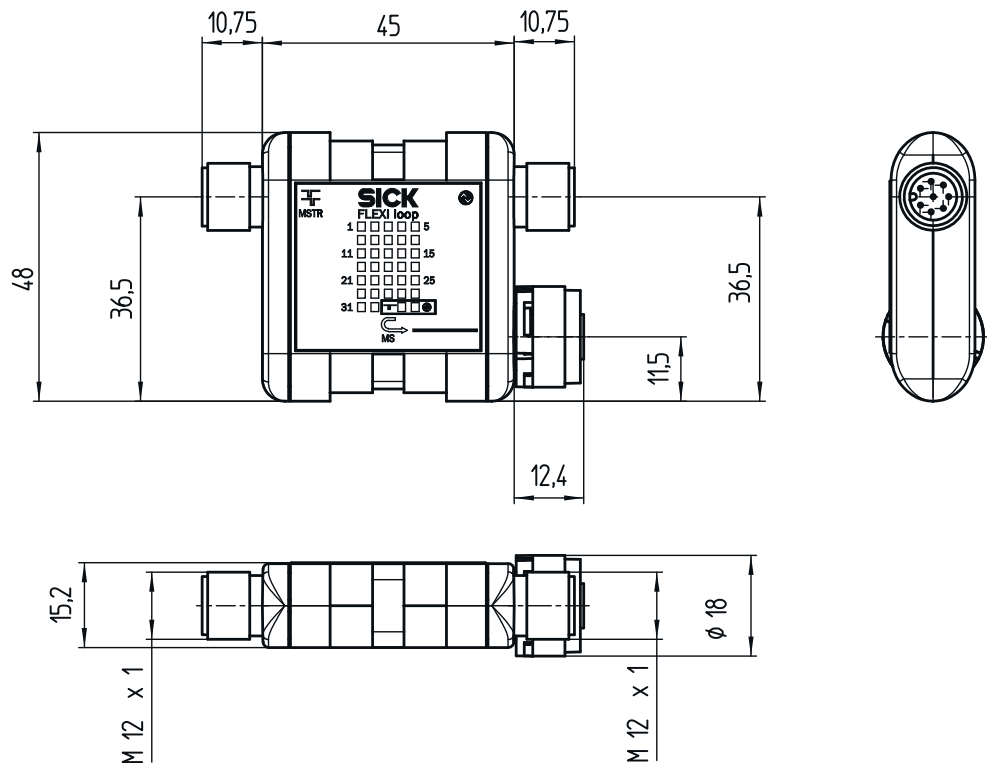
Plan coté des accessoires Flexi Loop FLA-MSTR00002 (mm)
